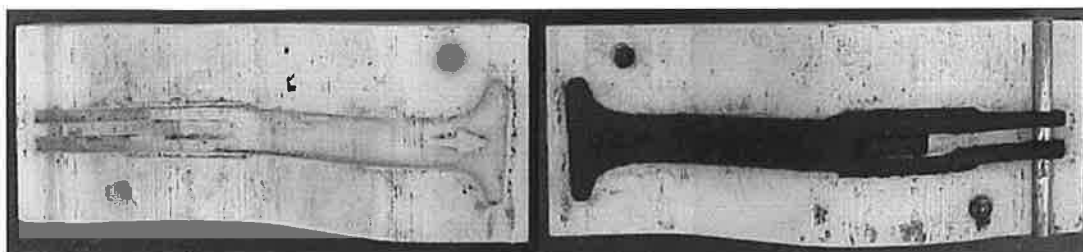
Molde de injeção pelo método direto. (Macarrão e Kaminski, 2003).
